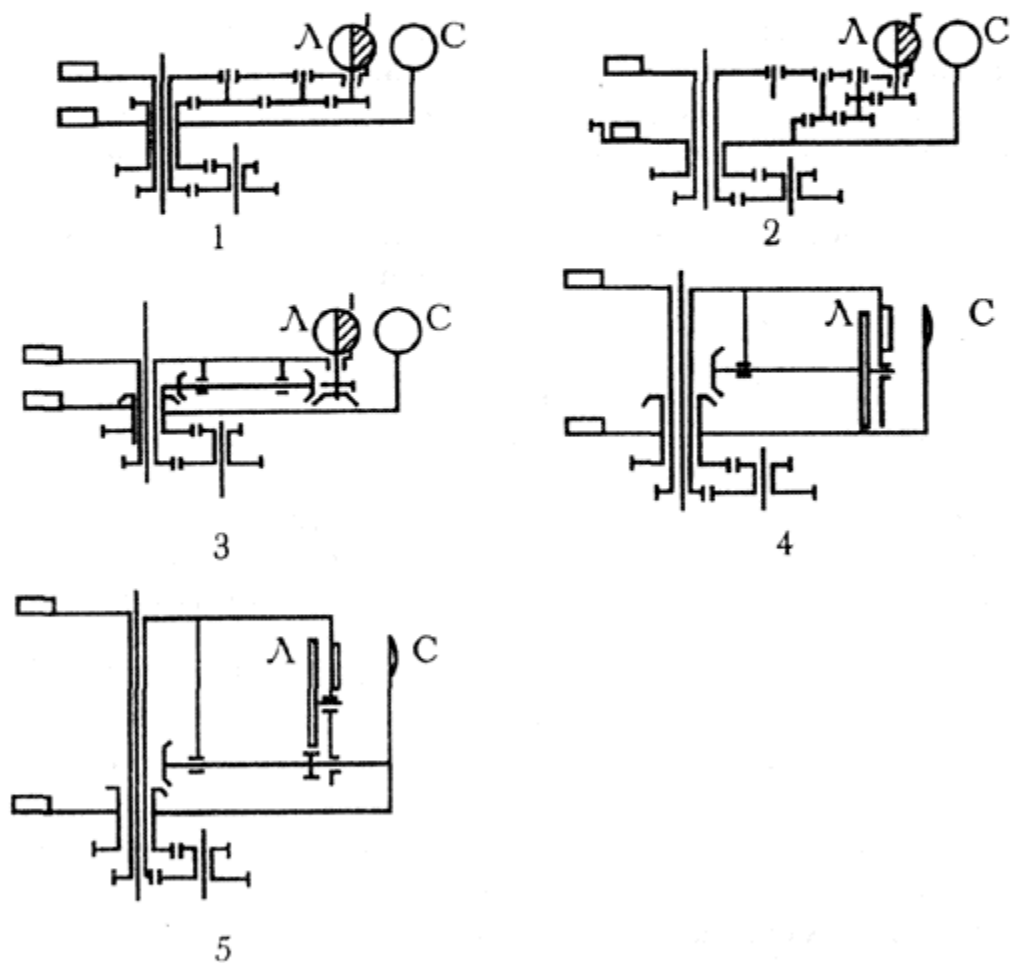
Варианты кинематики механизмов для изображения фаз Луны. 1 – планетарный механизм с цилиндрическими колесами для поворота шара, 2 – вариант предыдущего с дополнительной понижающей передачей, 3 – вариант первого с использованием конических колес и поперечного валика, 4 – прямая передача на шторку с масками через конические колеса, 5 – вариант предыдущего с дополнительной понижающей передачей, с – макет Солнца, л – макет Луны.
